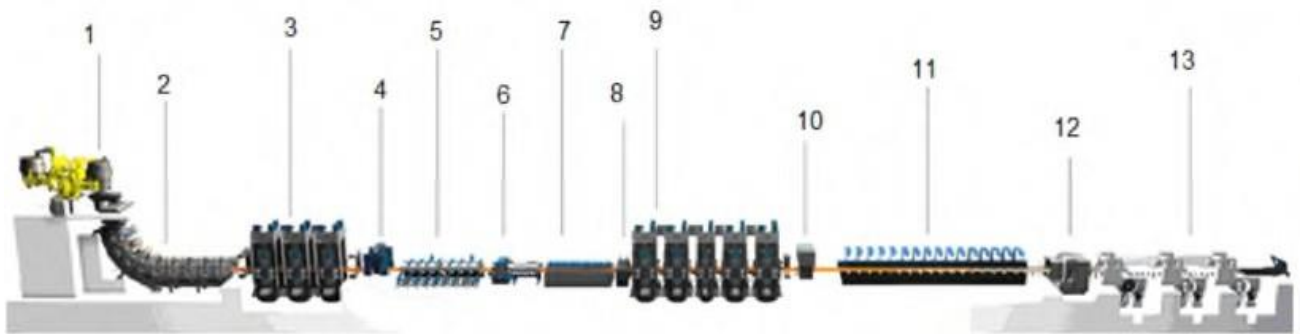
Схема агрегату ISP: 1 – розливний і проміжний ківш; 2 – кристалізатор машини з обтискними роликками; 3 – чорнова група прокатних клітей; 4 – ножиці; 5 – ділянка видачі листів; 6 – ножиці для розрізання; 7 – індукційний підігрів; 8 – гідросбівання окалини; 9 – чистова група прокатних клітей; 10 – блок для контролю листів; 11 – лінія ламінарного охолодження; 12 – летючі ножиці; 13 – моталки
